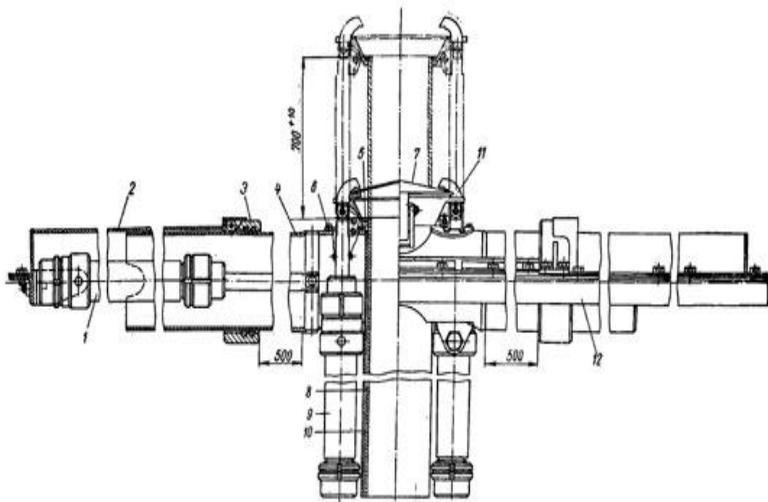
Прибор для нижнего слива нефтепродуктов из вагонов-цистерн: 1 – гидроцилиндр горизонтального перемещения сливной трубы; 2 – кожух; 3 – обойма с уплотнениями; 4 – цилиндр горизонтальный; 5 – уплотнение; 6 – накладка; 7 – крышка двухстворчатая; 8 – сливная труба; 9 – гидроцилиндр вертикального перемещения сливной трубы; 10 – цилиндр сливной трубы; 11 – защелка; 12 – рама сливного прибора.
